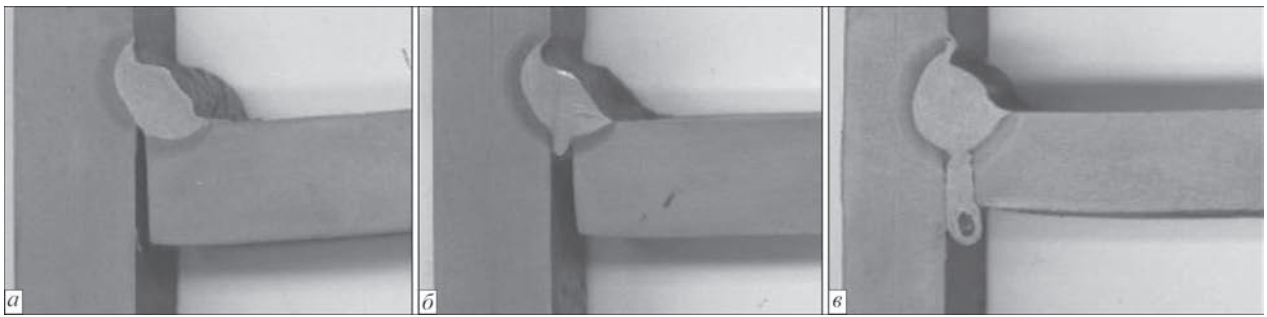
Примеры сварных соединений образцов с различными параметрами сборки и сварки
